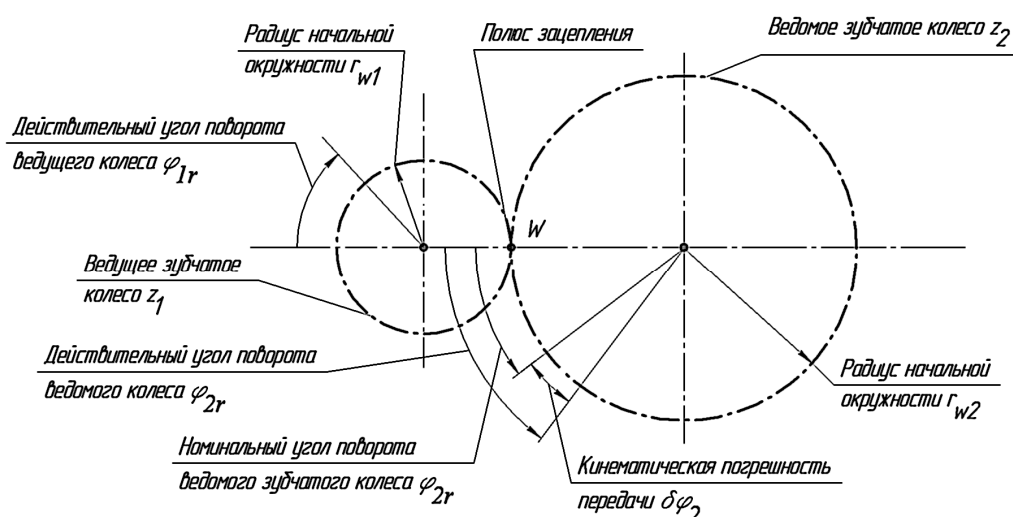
Понятие кинематической погрешности зубчатой передачи.
